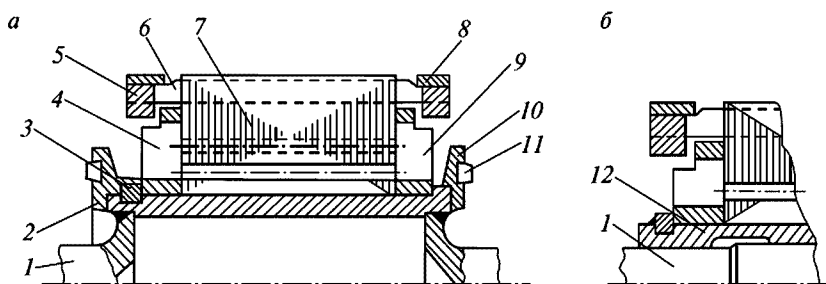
Конструкция ротора асинхронного тягового электродвигателя: 1 — вал; 3 — шпонка; 4, 9 — нажимные шайбы; 5 — короткозамкнутые кольца обмотки ротора; 6 — стержни обмотки; 7 — сердечник; 8 — бандажные кольца; 10, 2 — специальные диски; 11 — дополнительные грузы для динамической балансировки; 12 — втулка
